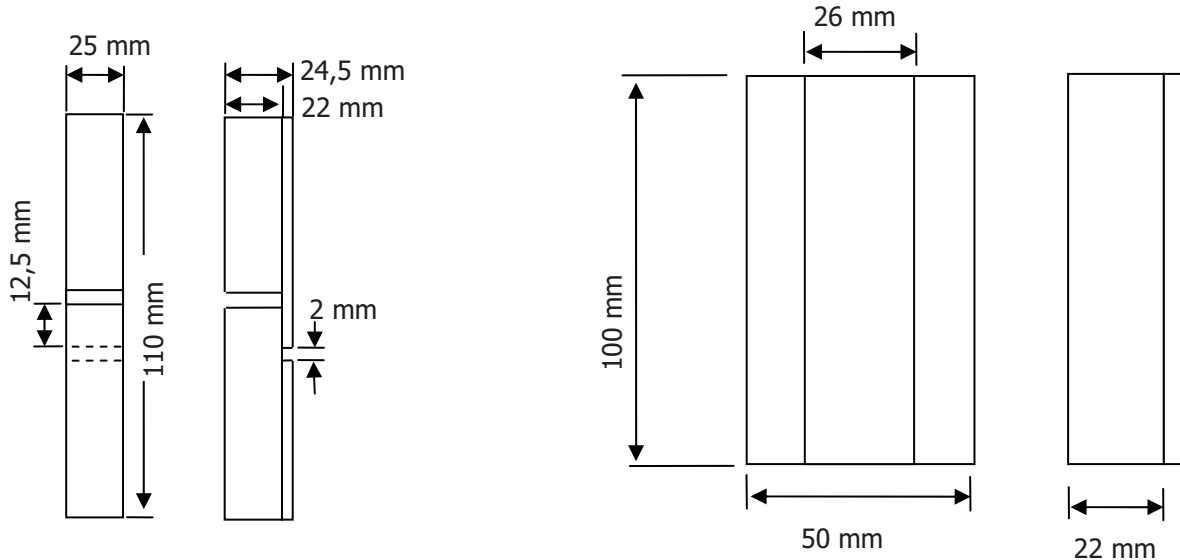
Druck-Prüfgeometrie für APC2-450CA30 Schweißungen in Anlehnung an die *QVA-Z10-46-09
